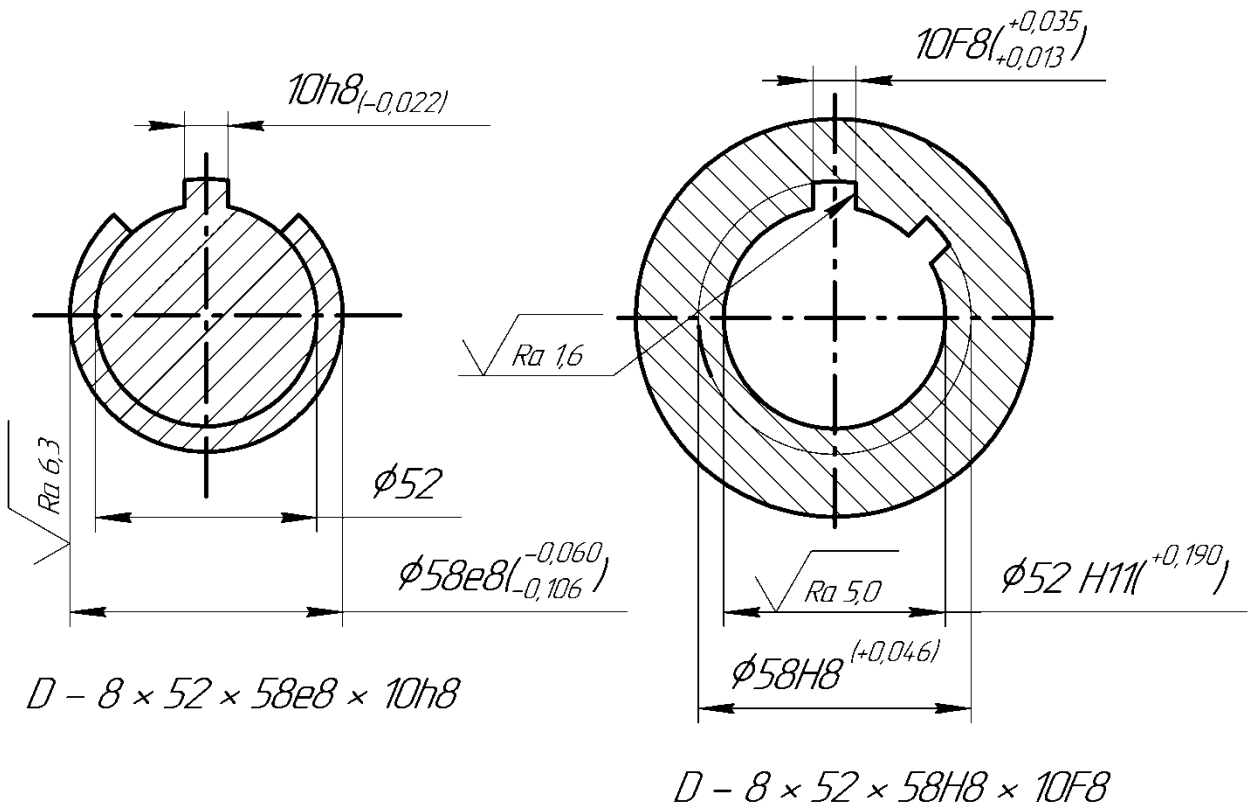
Обозначение допусков и предельных отклонений на рабочих чертежах деталей шлицевого соединения
